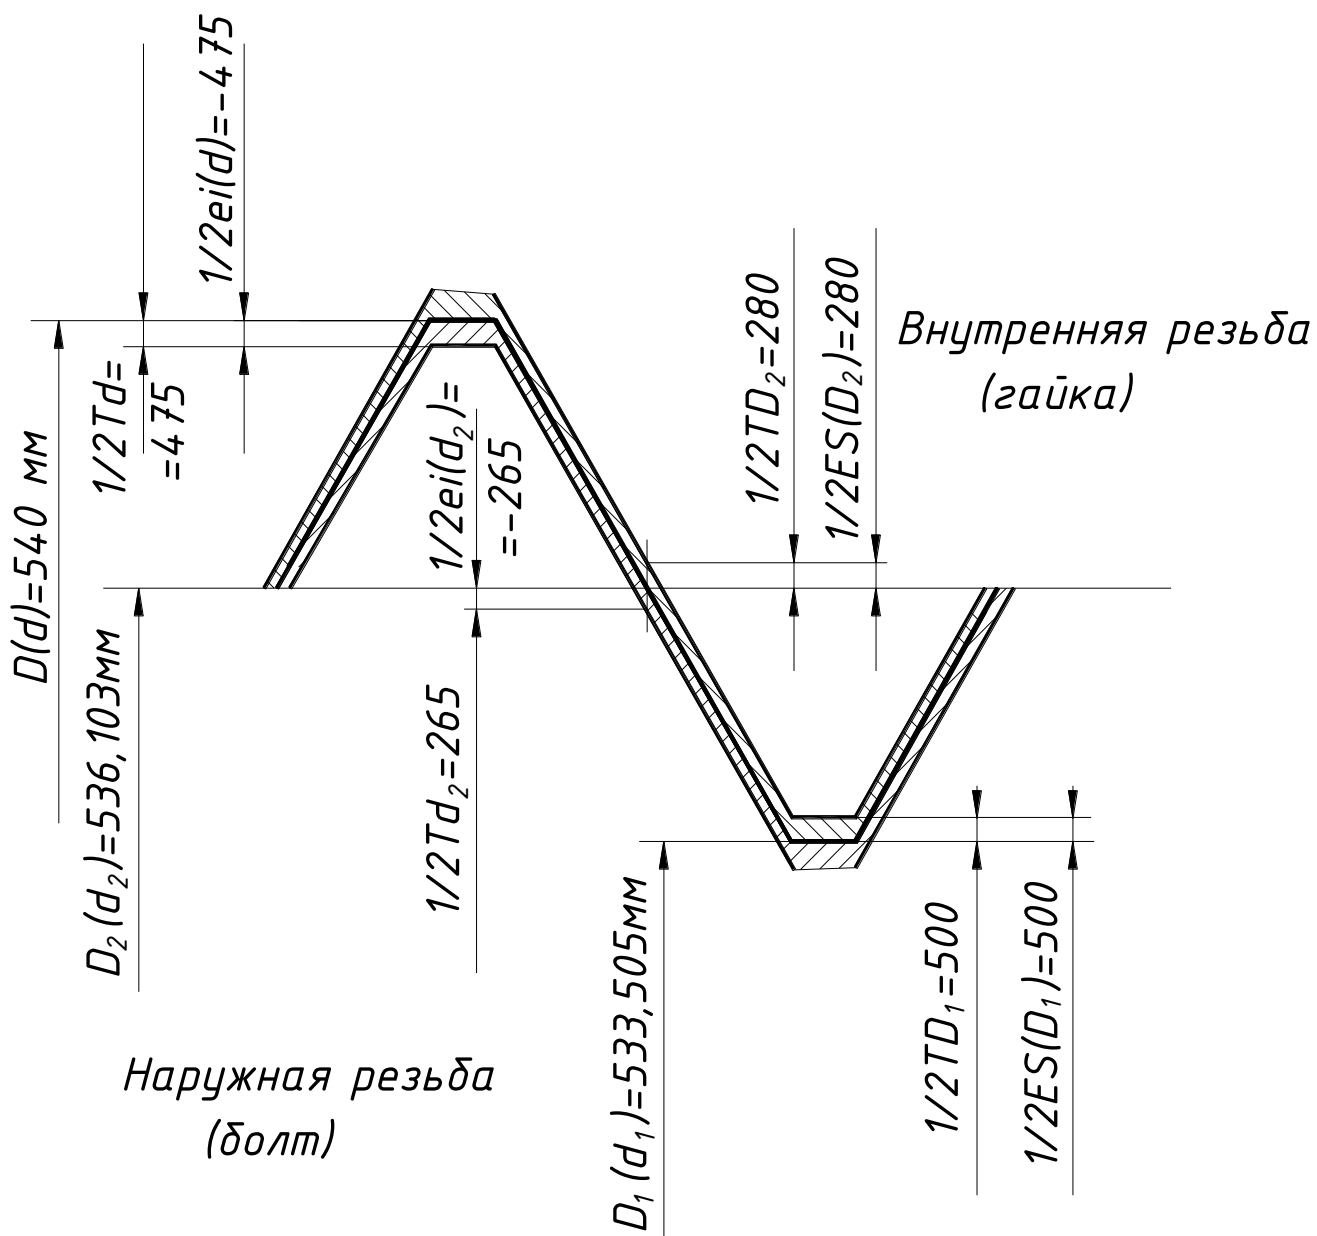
Схема розташування полів допусків різьблення
